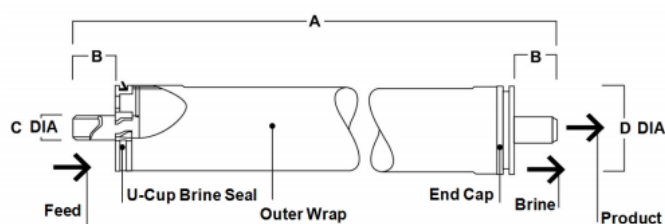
Dimension de la Membrane de type RO-4040-F
